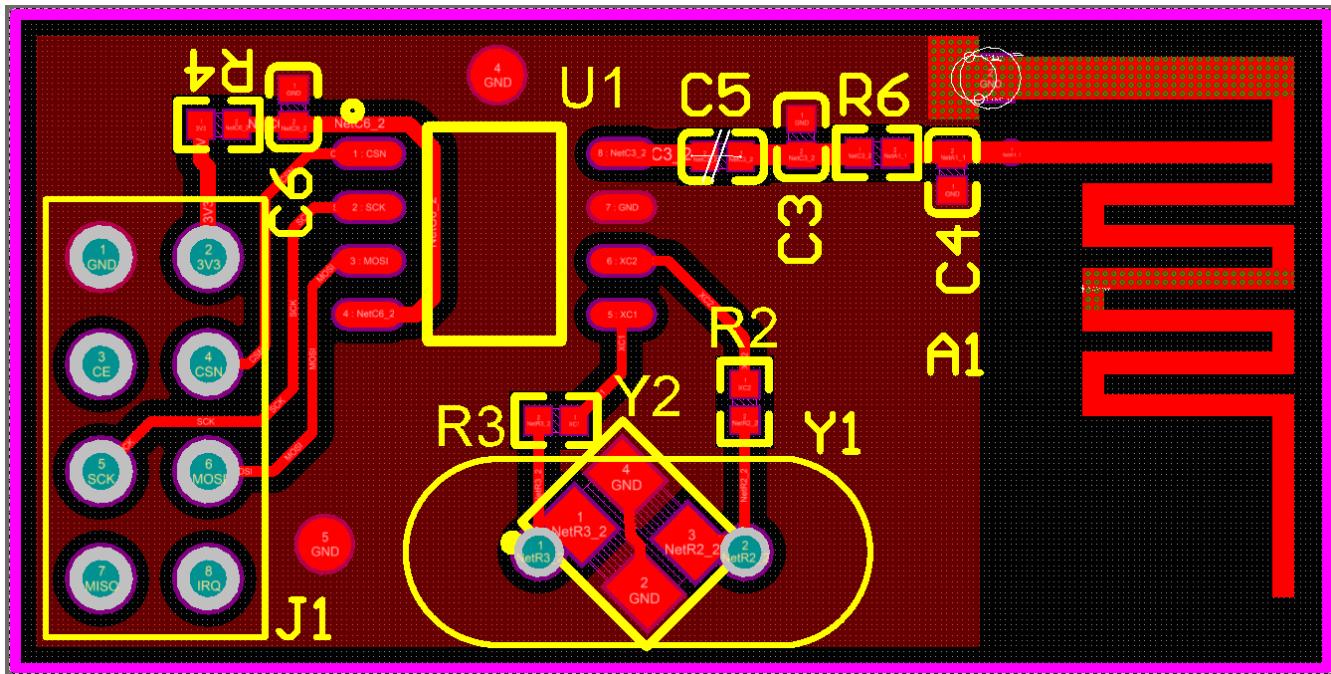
PAN1026 SOP8 封装 LAYOUT 示例
